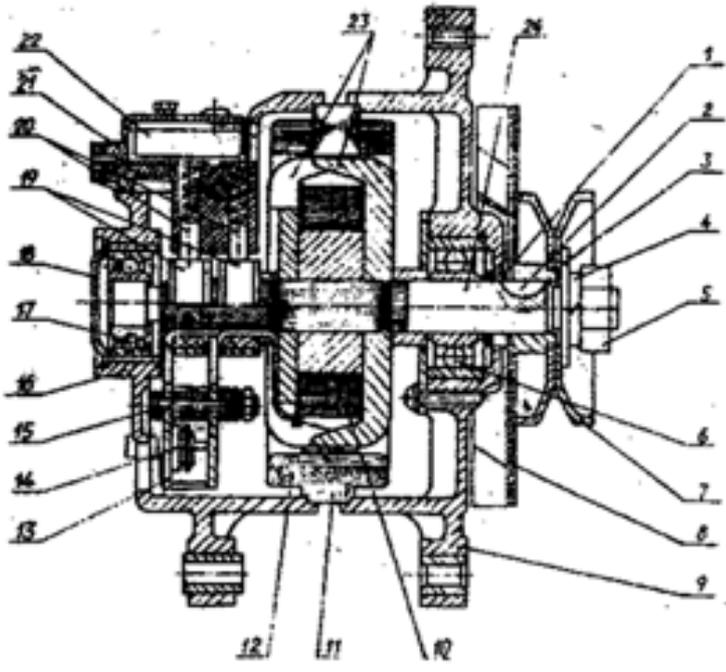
Генератор 583.3701: 1 - втулка; 2 - шпонка; 3 - шайба; 4 - стопорная шайба; 5 - гайка; 6, 17 - передний и задний подшипники; 7 - шкив; 8 - вентилятор; 9, 16 - крышки со стороны привода и контактных колец; 10 - катушка возбуждения; 11 - статор; 12 - обмотка статора; 13 - выпрямительный блок; 14 - диод; 15 - контактный болт; 18 - крышка подшипника; 19 - контактные кольца; 20 - щетки; 21 - щеткодержатель; 22 - интегральное устройство регулятора напряжения; 23 - полюсные наконечники ротора; 24 - вал ротора; 25 - винт; 26 - конденсатор; "+", "~-~", "ш" - выводы генератора
